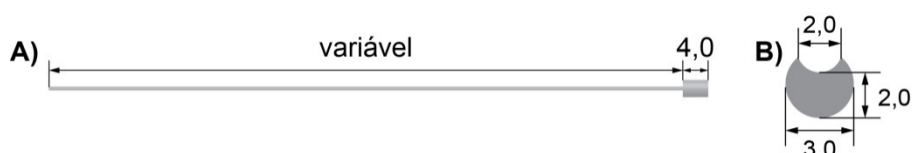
Dimensões dos limitadores, em centímetros: A) vista lateral; B) vista frontal.
